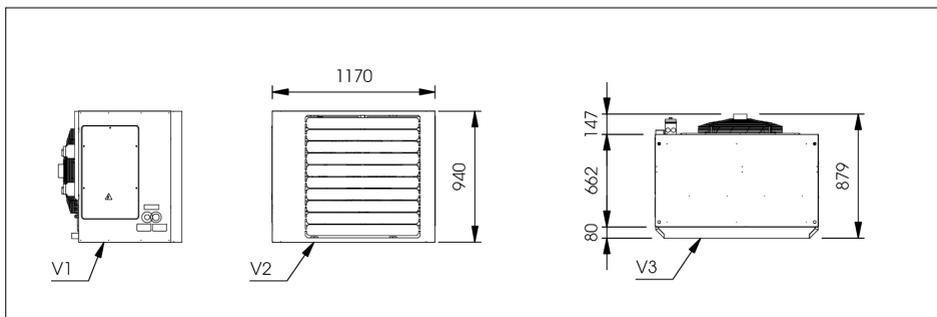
Dimensions du MISTRAL MDX 30. (V1 : Vue latérale gauche, V2 : Vue de face, V3 : Vue de dessus)
